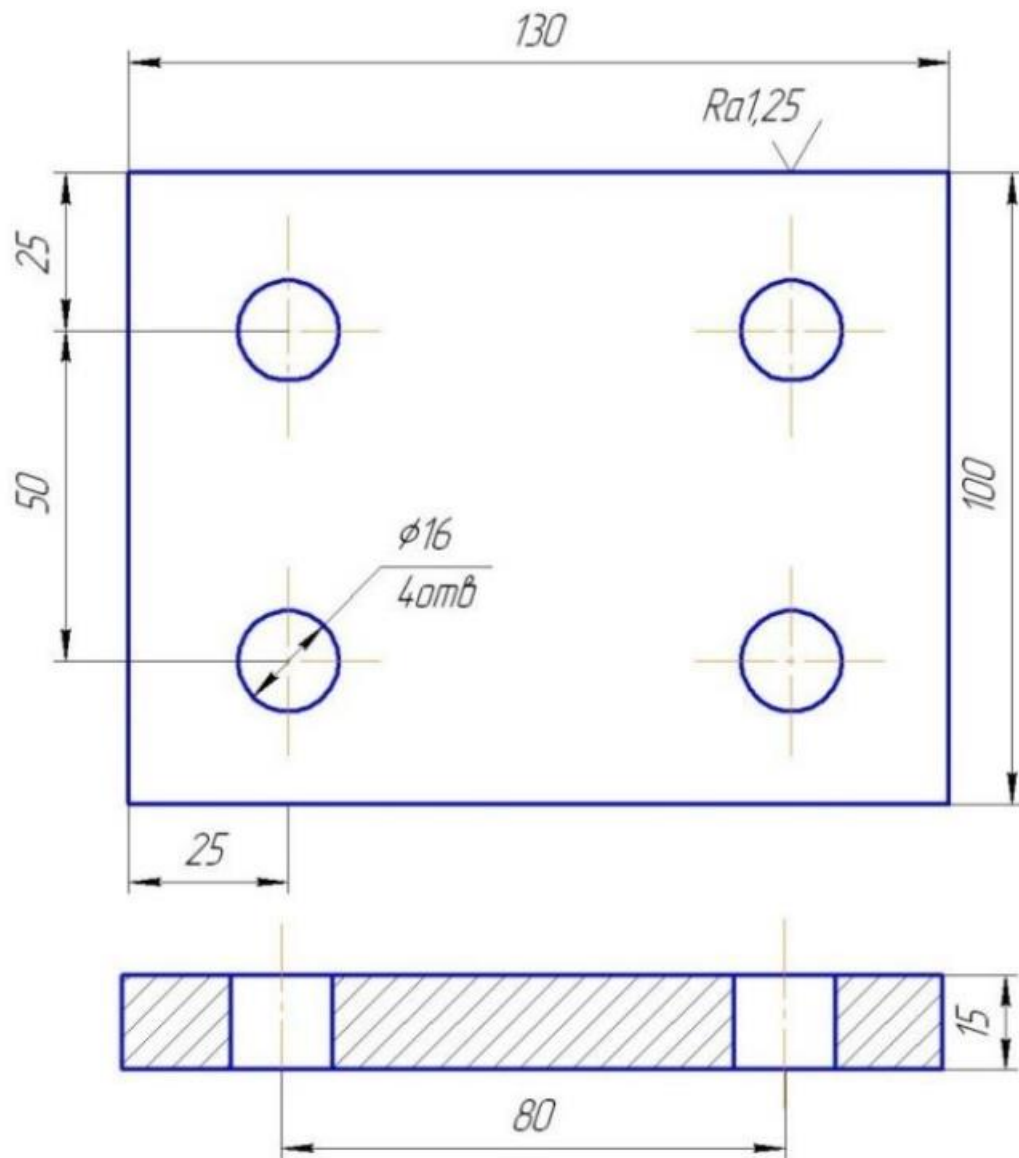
Креслення опорної пластини (деталювання)
